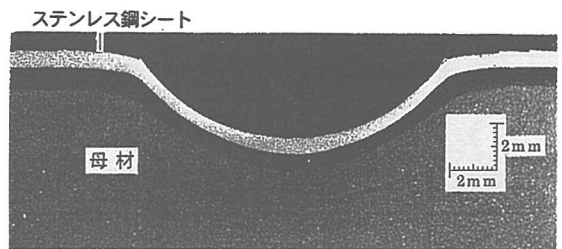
衝撃試験片の断面拡大写真（溶接部）
